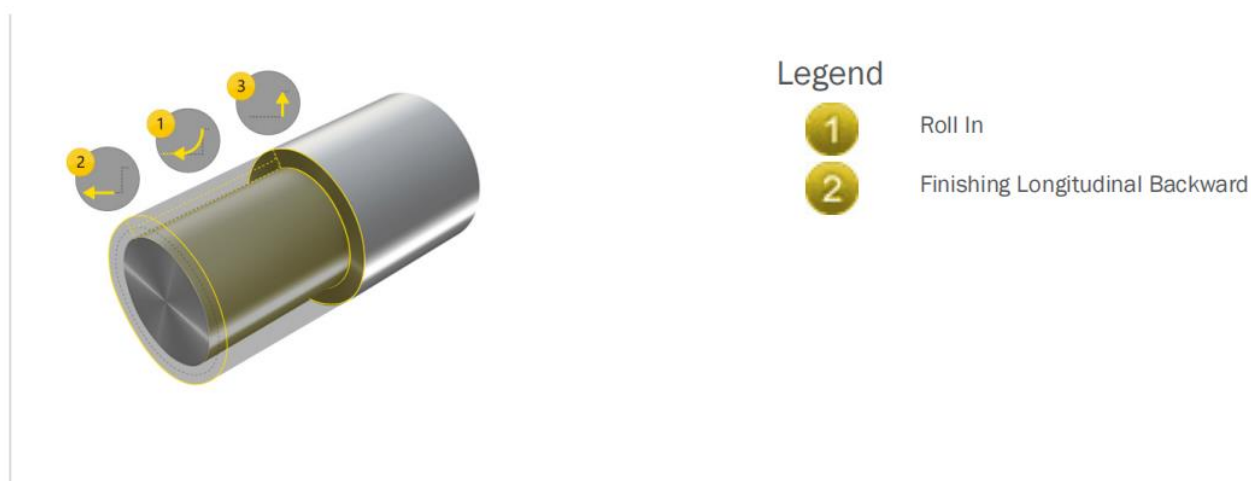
Схема маршруту обробки для поверхні 1 у програмі Sandvik Tool Guide
